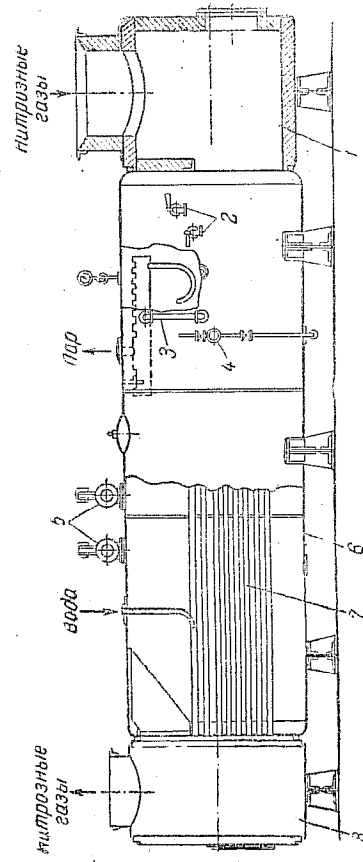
Котел-утилизатор (поверхность нагрева 144 м²):
